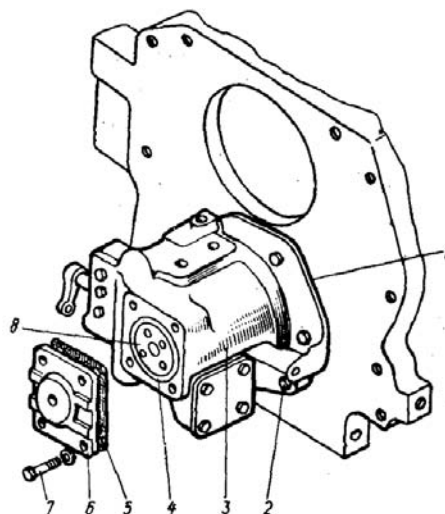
Установка гидрораспределителя: 1, 5 — прокладка; 2, 7 — болт; 3 — гидрораспределитель; 4 — кольцо; 6 — крышка; 8 — вал
